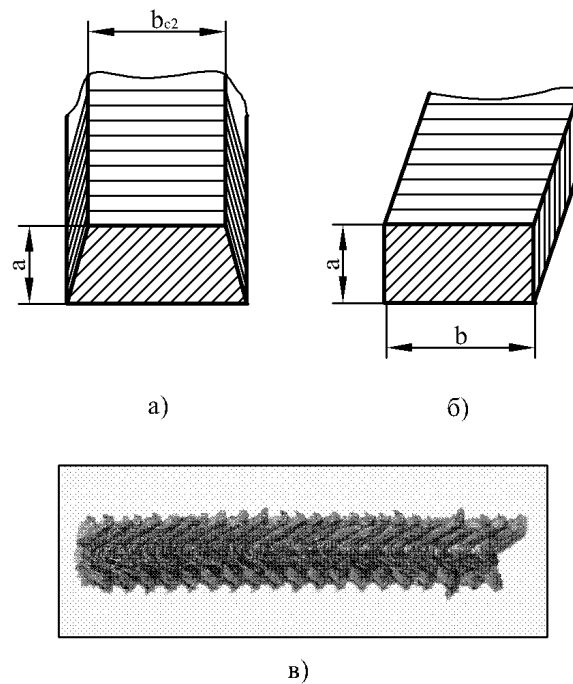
Форма (а, б) и фотография стружки при нарезании резьбы токарным резьбовым резцом:
